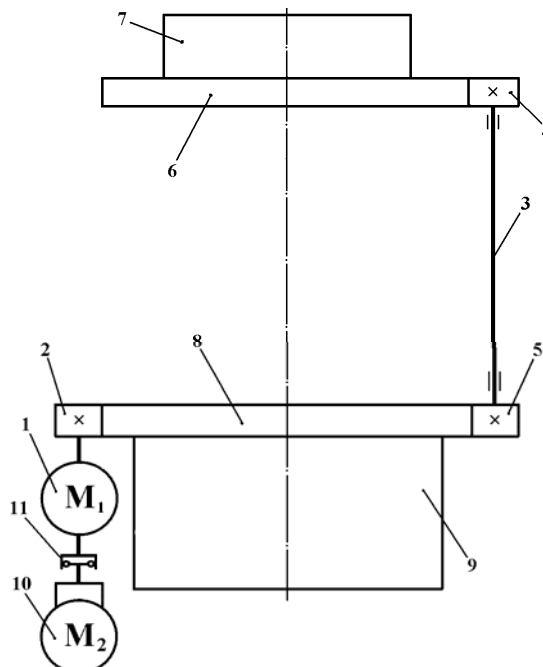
Кінематична схема привода круглов'язальної машини типу КО:
